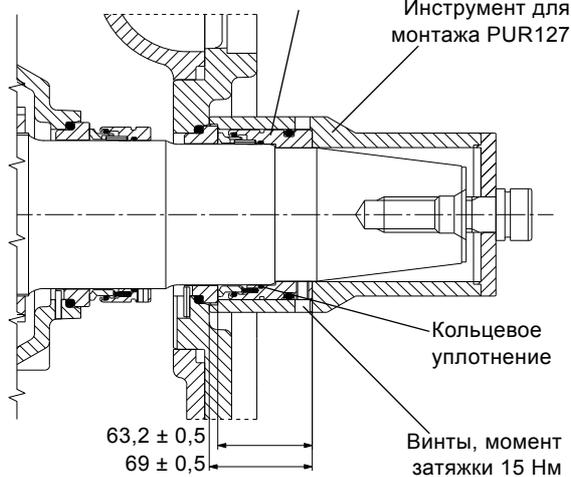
Установка вращающейся части первичного уплотнения вала, типоразмер 74
